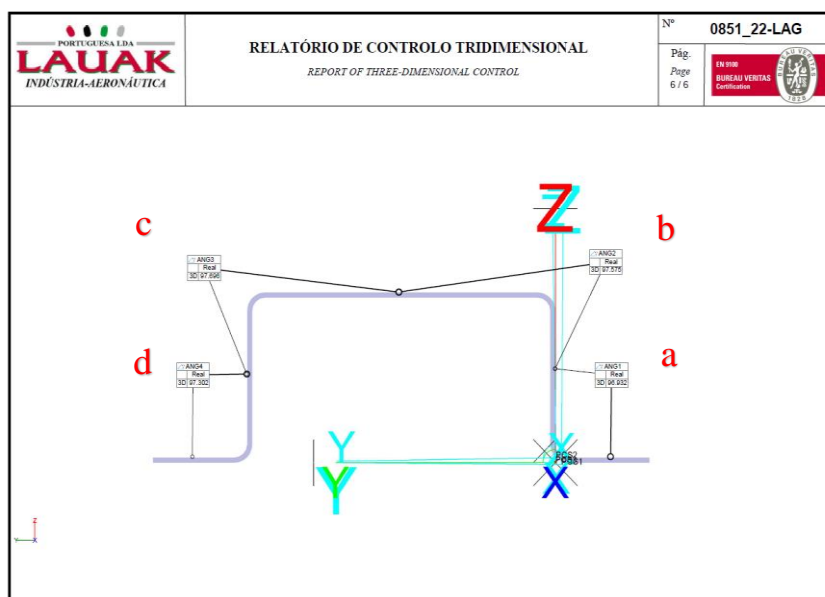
Desenho de uma chapa quinada com controlo dimensional – exemplo dos desvios angulares na chapa nº 50²⁸
